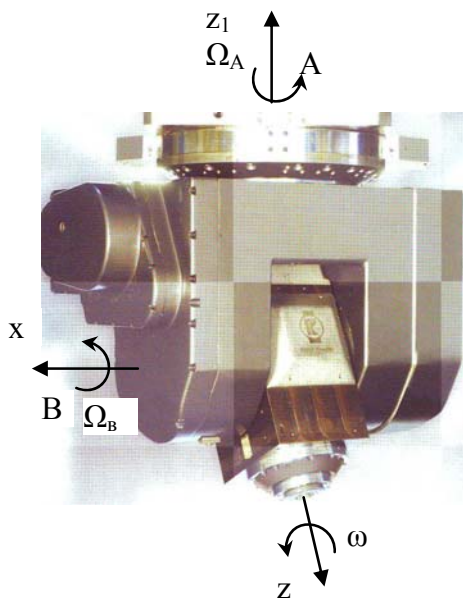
Схема поворотних рухів фрезерувальної головки по координатах A і B
